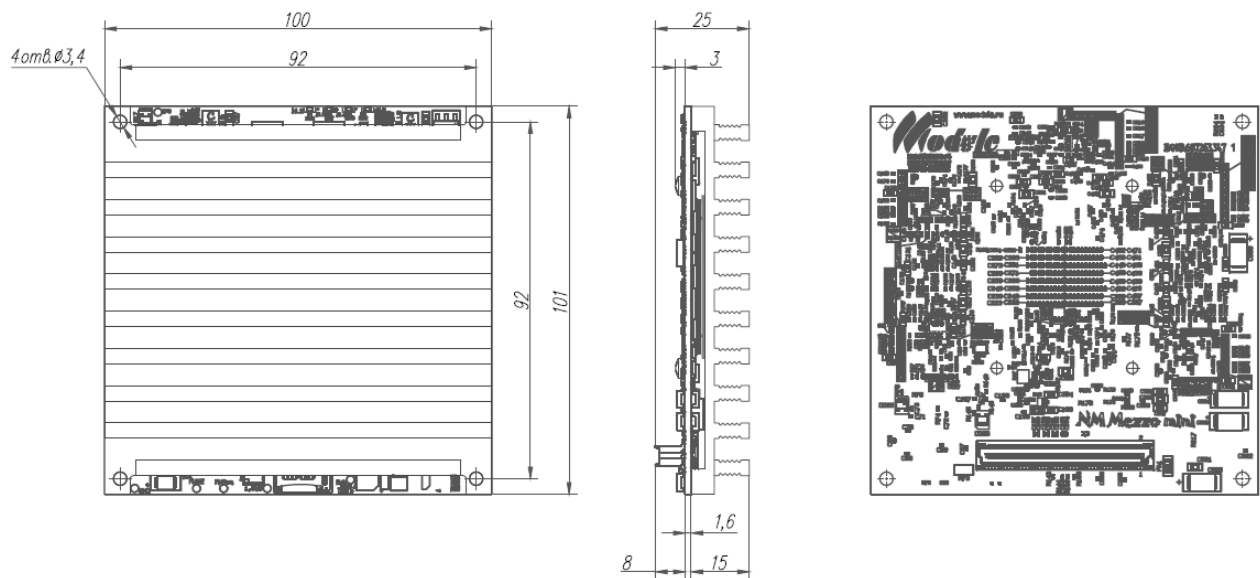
Габаритные и присоединительные размеры Модуля
